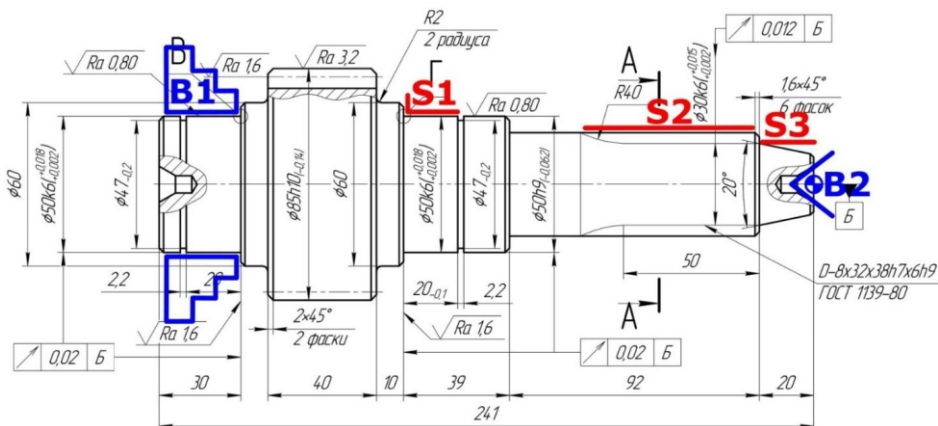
Графическое представление чертежа вала с обозначением схемы базирования обрабатываемых поверхностей и ноля системы координат заготовки
